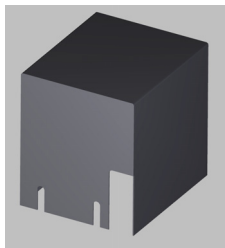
Rückseite der Haube mit Aussparungen für Kabel und Kühlschläuche
